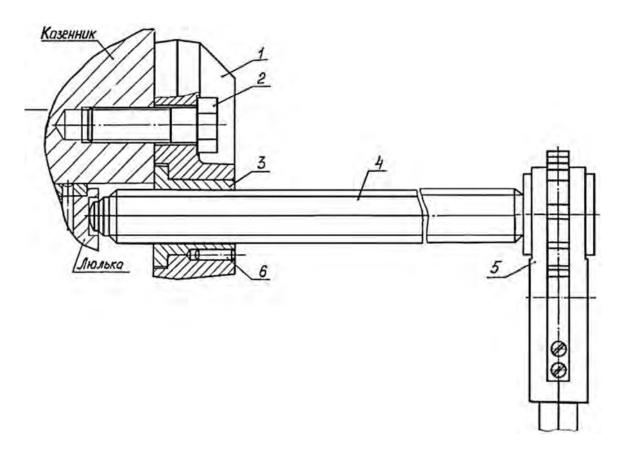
Установка прибора для оттягивания ствола: I – опора; 2, 4 – винты; 3 – матка; 5 – ключ-трещотка РГ 1; 6 – штифт
